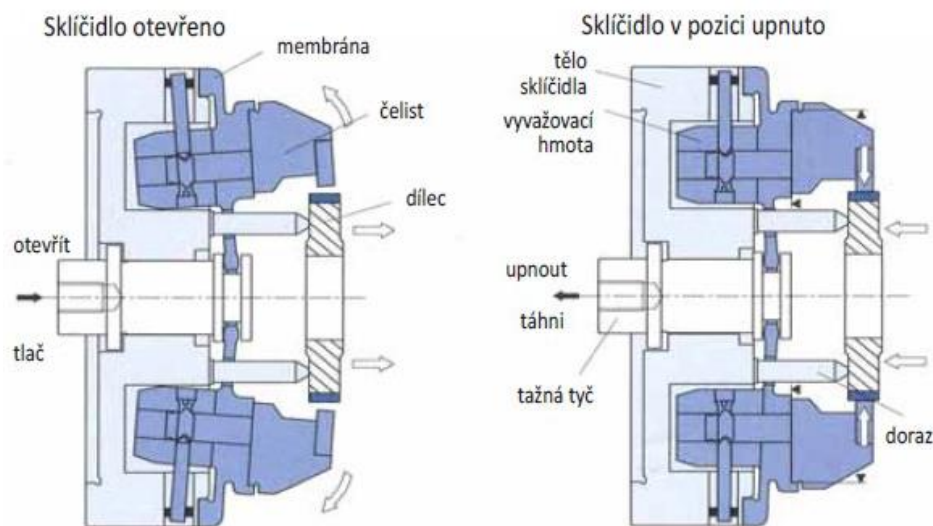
Hydraulické sklíčidlo Kitagawa BR08 [8]
